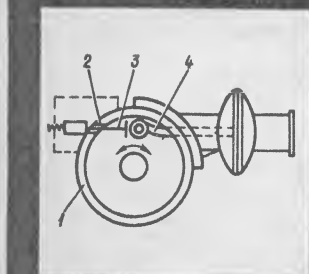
Установка переменного резистора в корпус распределителя: 1 — корпус распределителя; 2 — отверстие в корпусе; 3 — переменный резистор; 4 — шток вакуум-корректора
